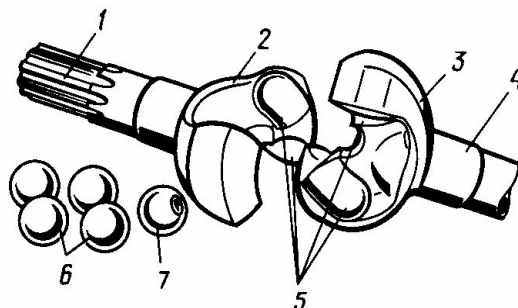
Четырехшариковый карданный шарнир с делительными канавками (типа «Вейс») 1, 4 – вал; 2, 3 – кулак; 5 – канавки; 6, 7 – шарики.
